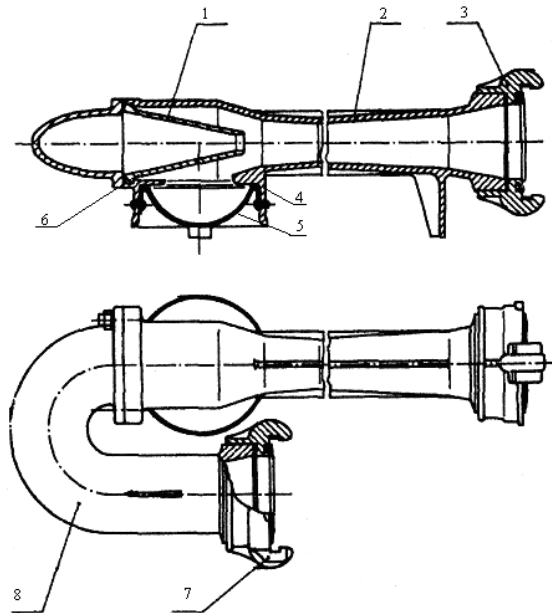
Будова пожежного гідроелеватора: 1 — сопло; 2 — дифузор; 3 — головка з'єднувальна ГМН-80; 4 — обичайка; 5 — сітка; 6 — кільце ущільнююче; 7 – головка з'єднувальна ГМН-70; 8 – коліно
